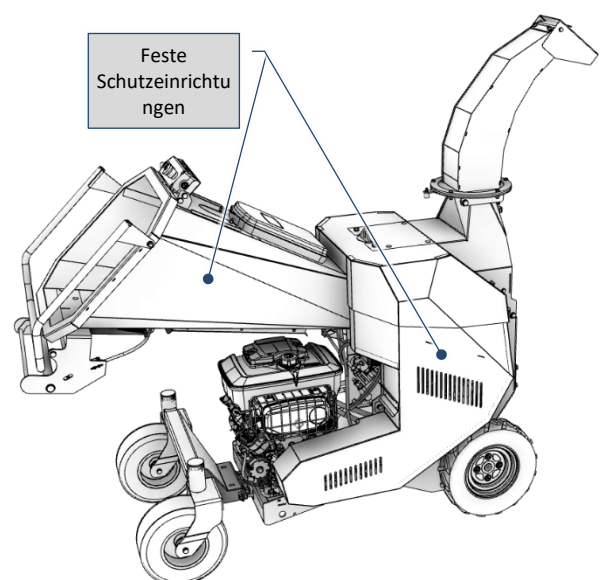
Feste Schutzeinrichtungen der Maschine (Rechte Seitenansicht)
